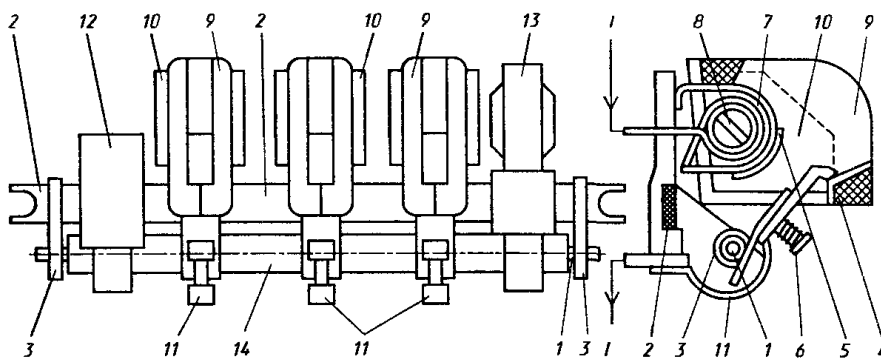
Конструктивна схема контактора КТ6000
